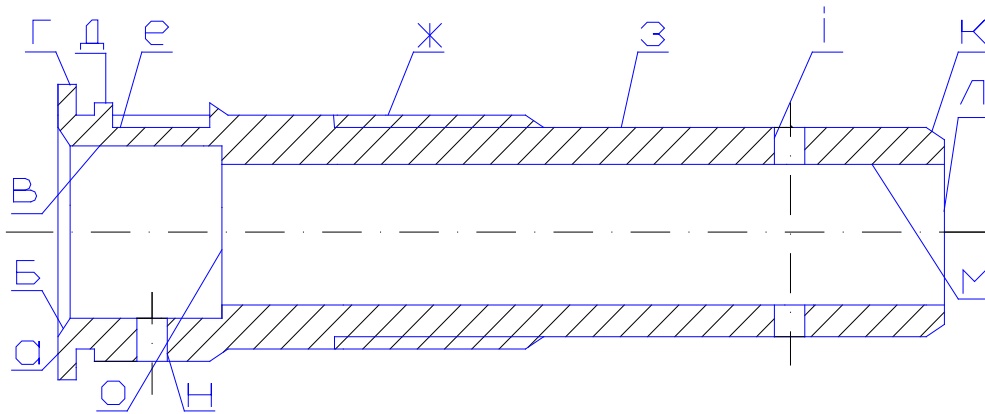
Креслення деталі з закодованими поверхнями
